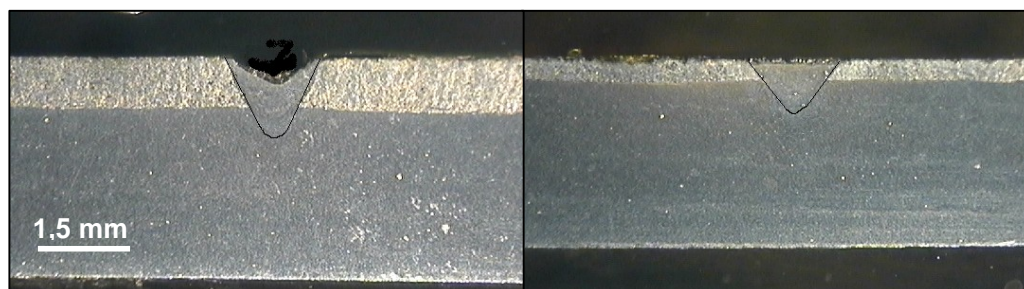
Macrografias de seções transversais de soldagem laser com 2000 W sobre revestimento aspergido com espessura de 1,0 mm e 0,4 mm.
